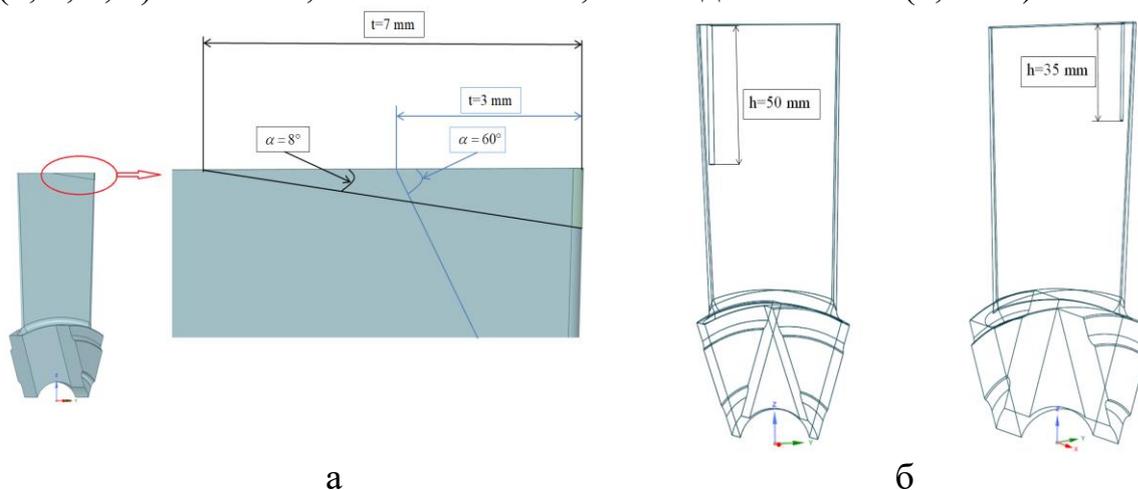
Виды геометрических изменений (а – скос верхней кромки лопатки; б – сверление отверстия в лопатках)
